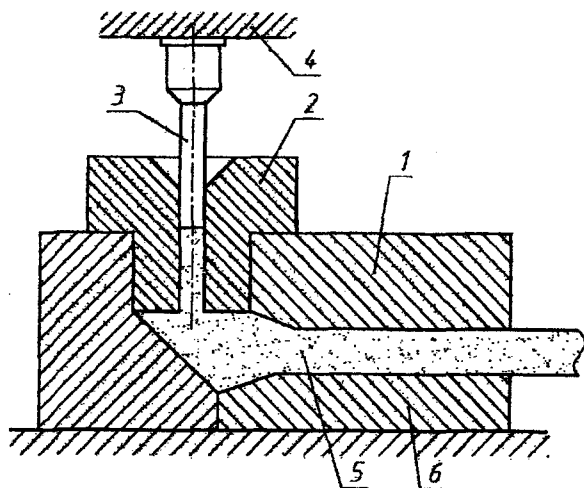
Способ формования изделий большой длины при подаче порошка отдельными дозами: 1 – матрица; 2 – питатель с воронкой; 3 – пуансон; 4 – ползун пресса; 5 – изделие; 6 – стол пресса
